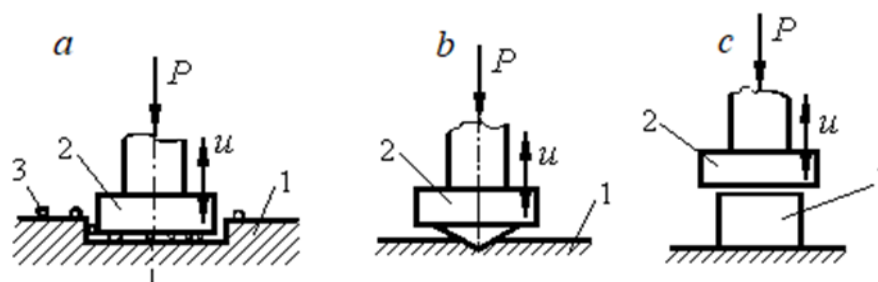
Ультразвуковая обработка: *a* - резание; *b* – поверхностное упрочнение; *c*- осадка металла.
